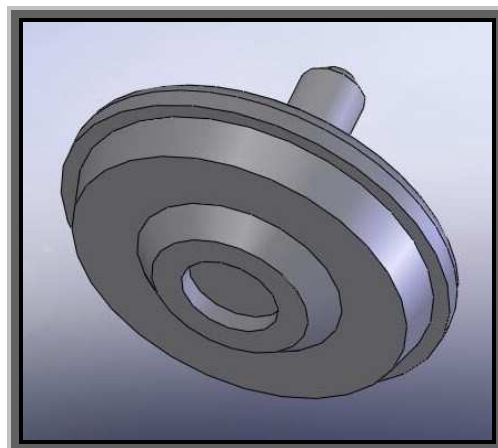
Vista isométrica de la estructura de acero del conjunto rueda giratoria.
